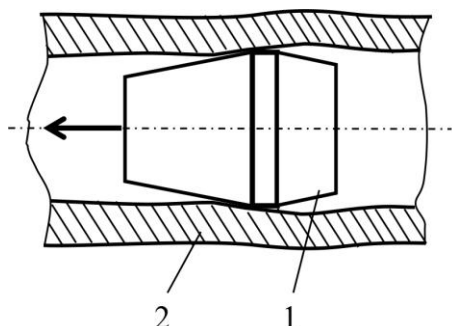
Схема деформуючого протягування: 1 – деформуючий інструмент; 2 – оброблювана деталь
